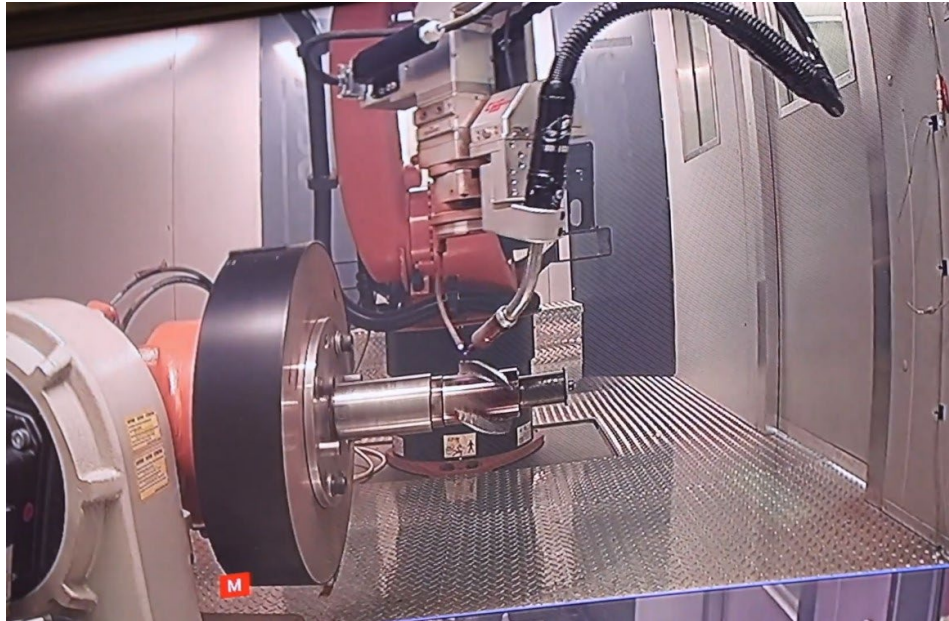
Процес виготовлення деталі за допомогою KUKA Robotics.
